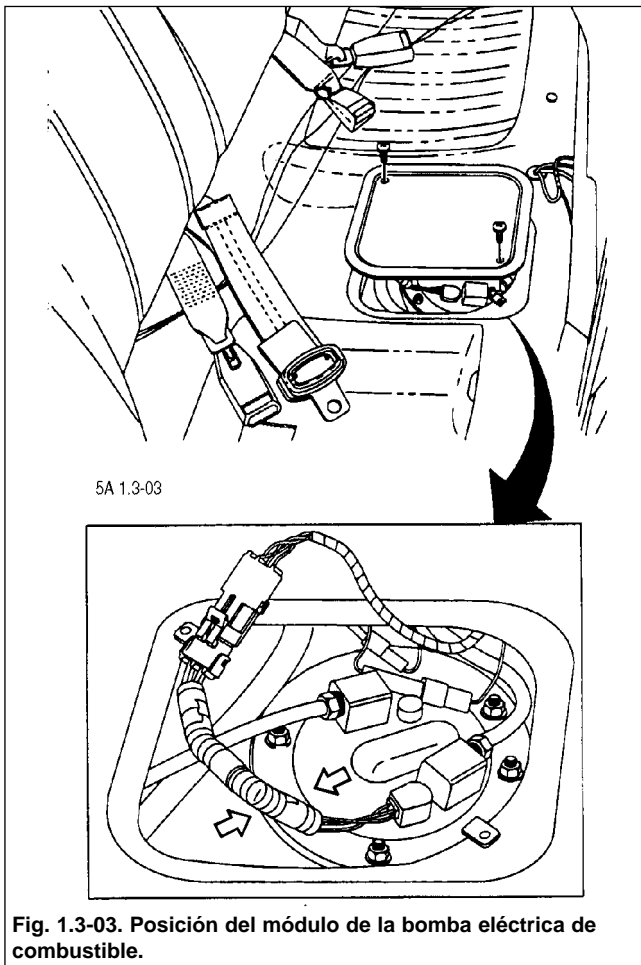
Posición del módulo de la bomba eléctrica de combustible.
